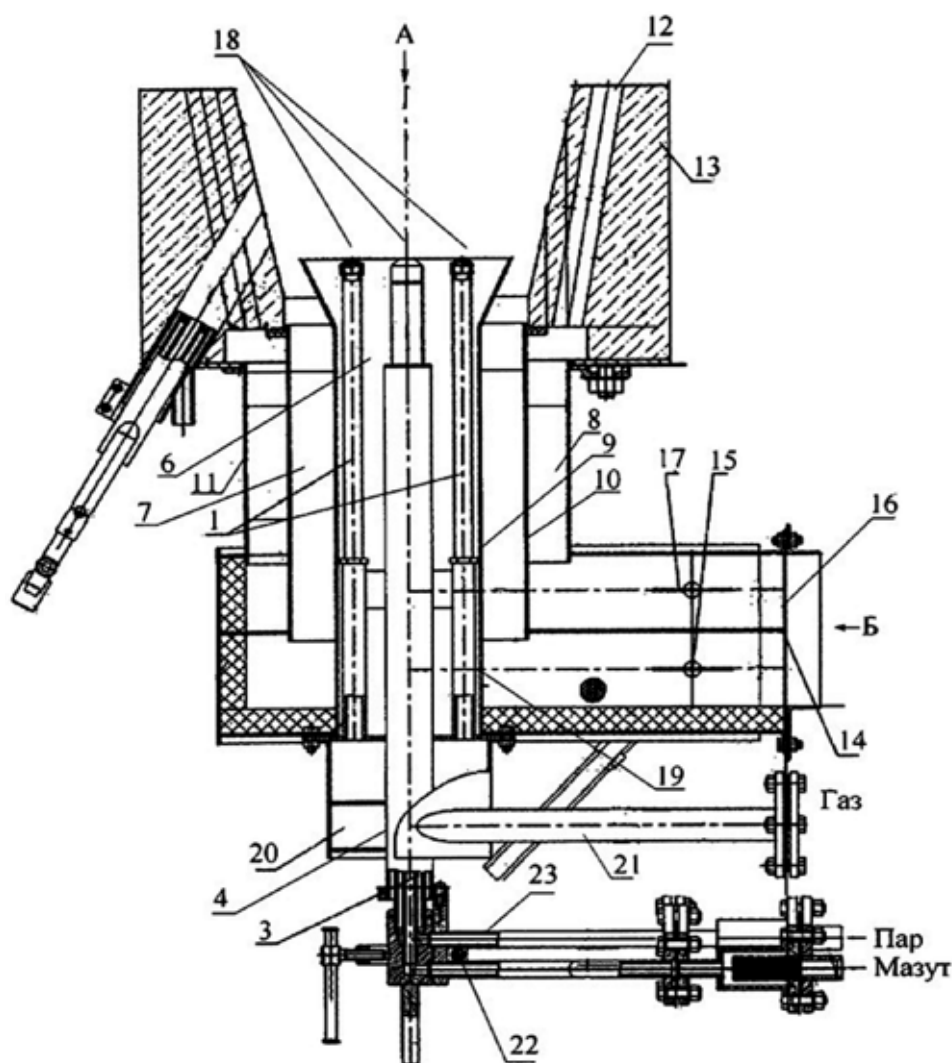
Горелочное устройство ГКВД (продольный разрез), состоящее из следующих элементов: 1 — газовые стволы; 2 — выходные отверстия для подачи газа; 3 — форсунка; 4 — центровочная труба; 6 — центральный канал; 7 — средний канал; 8 — периферийный канал; 9 — внутренняя обечайка; 10 — средняя обечайка; 11 — наружная обечайка; 12 — цилиндрические отверстия; 13 — горелочный камень; 14, 16 — воздуховод; 15, 17 — регулятор подачи воздуха; 18 — зона выходных отверстий 2; 19 — окна; 20 — газовая камера; 21 — газопроводящий патрубок; 22 — жиклер; 23 — эмульсатор.
